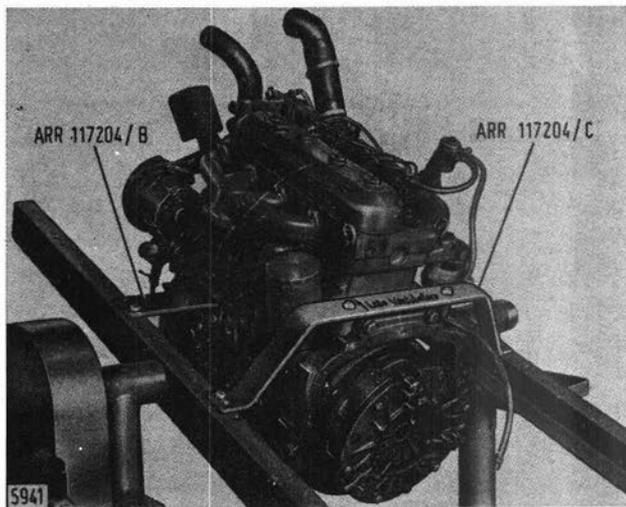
/7 - Fixation du moteur sur le chevalet rotatif ARR 2216 à l'aide des supports avant ARR 117204/A/B et de la potence arrière ARR 117204/C.
